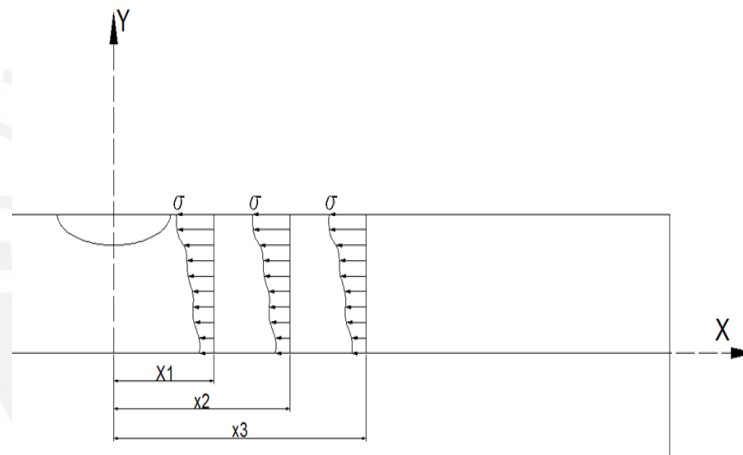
Esfuerzos normales al plano de la fisura
